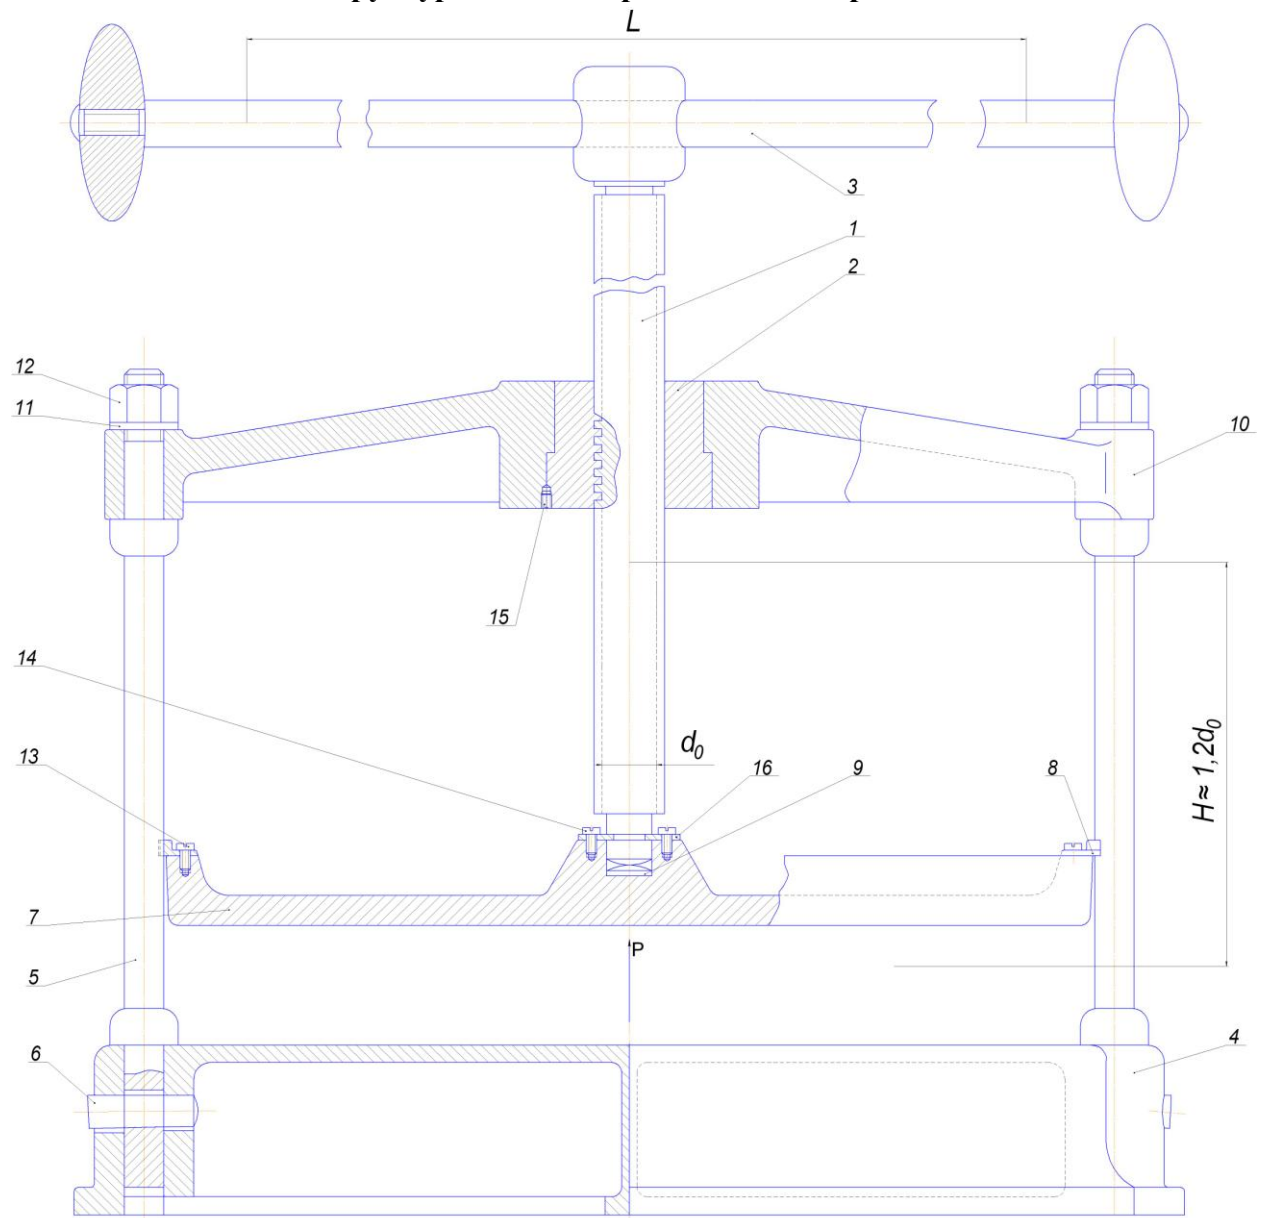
Винтовой пресс: 1 – винт; 2 – гайка; 3 – рукоятка; 4 – нижняя плита; 5 – колонки; 6 – клинья; 7 – подвижная плита; 8 – ползуны; 9 – подпятник; 10 – верхняя плита; 11 – шайбы; 12 – гайки; 13 – 15 – винты; 16 – разрезная шайба.
